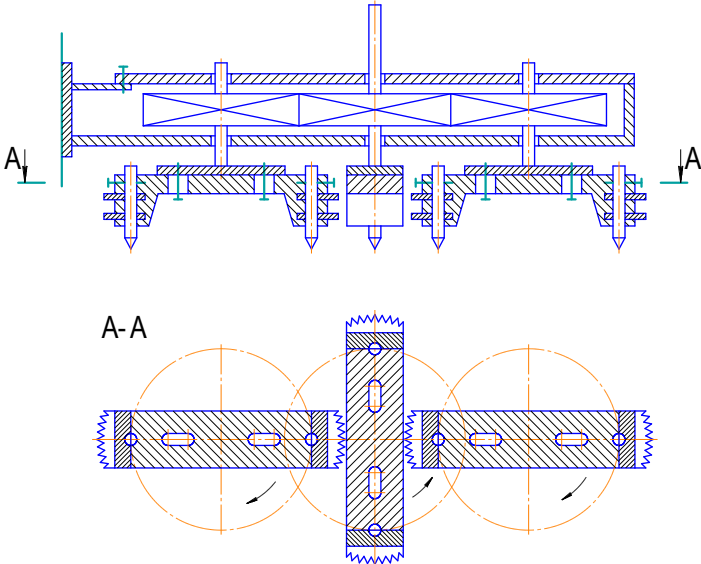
Фрезерна головка з перекриттям траєкторій фрез для однопрохідної обробки широких поверхонь
